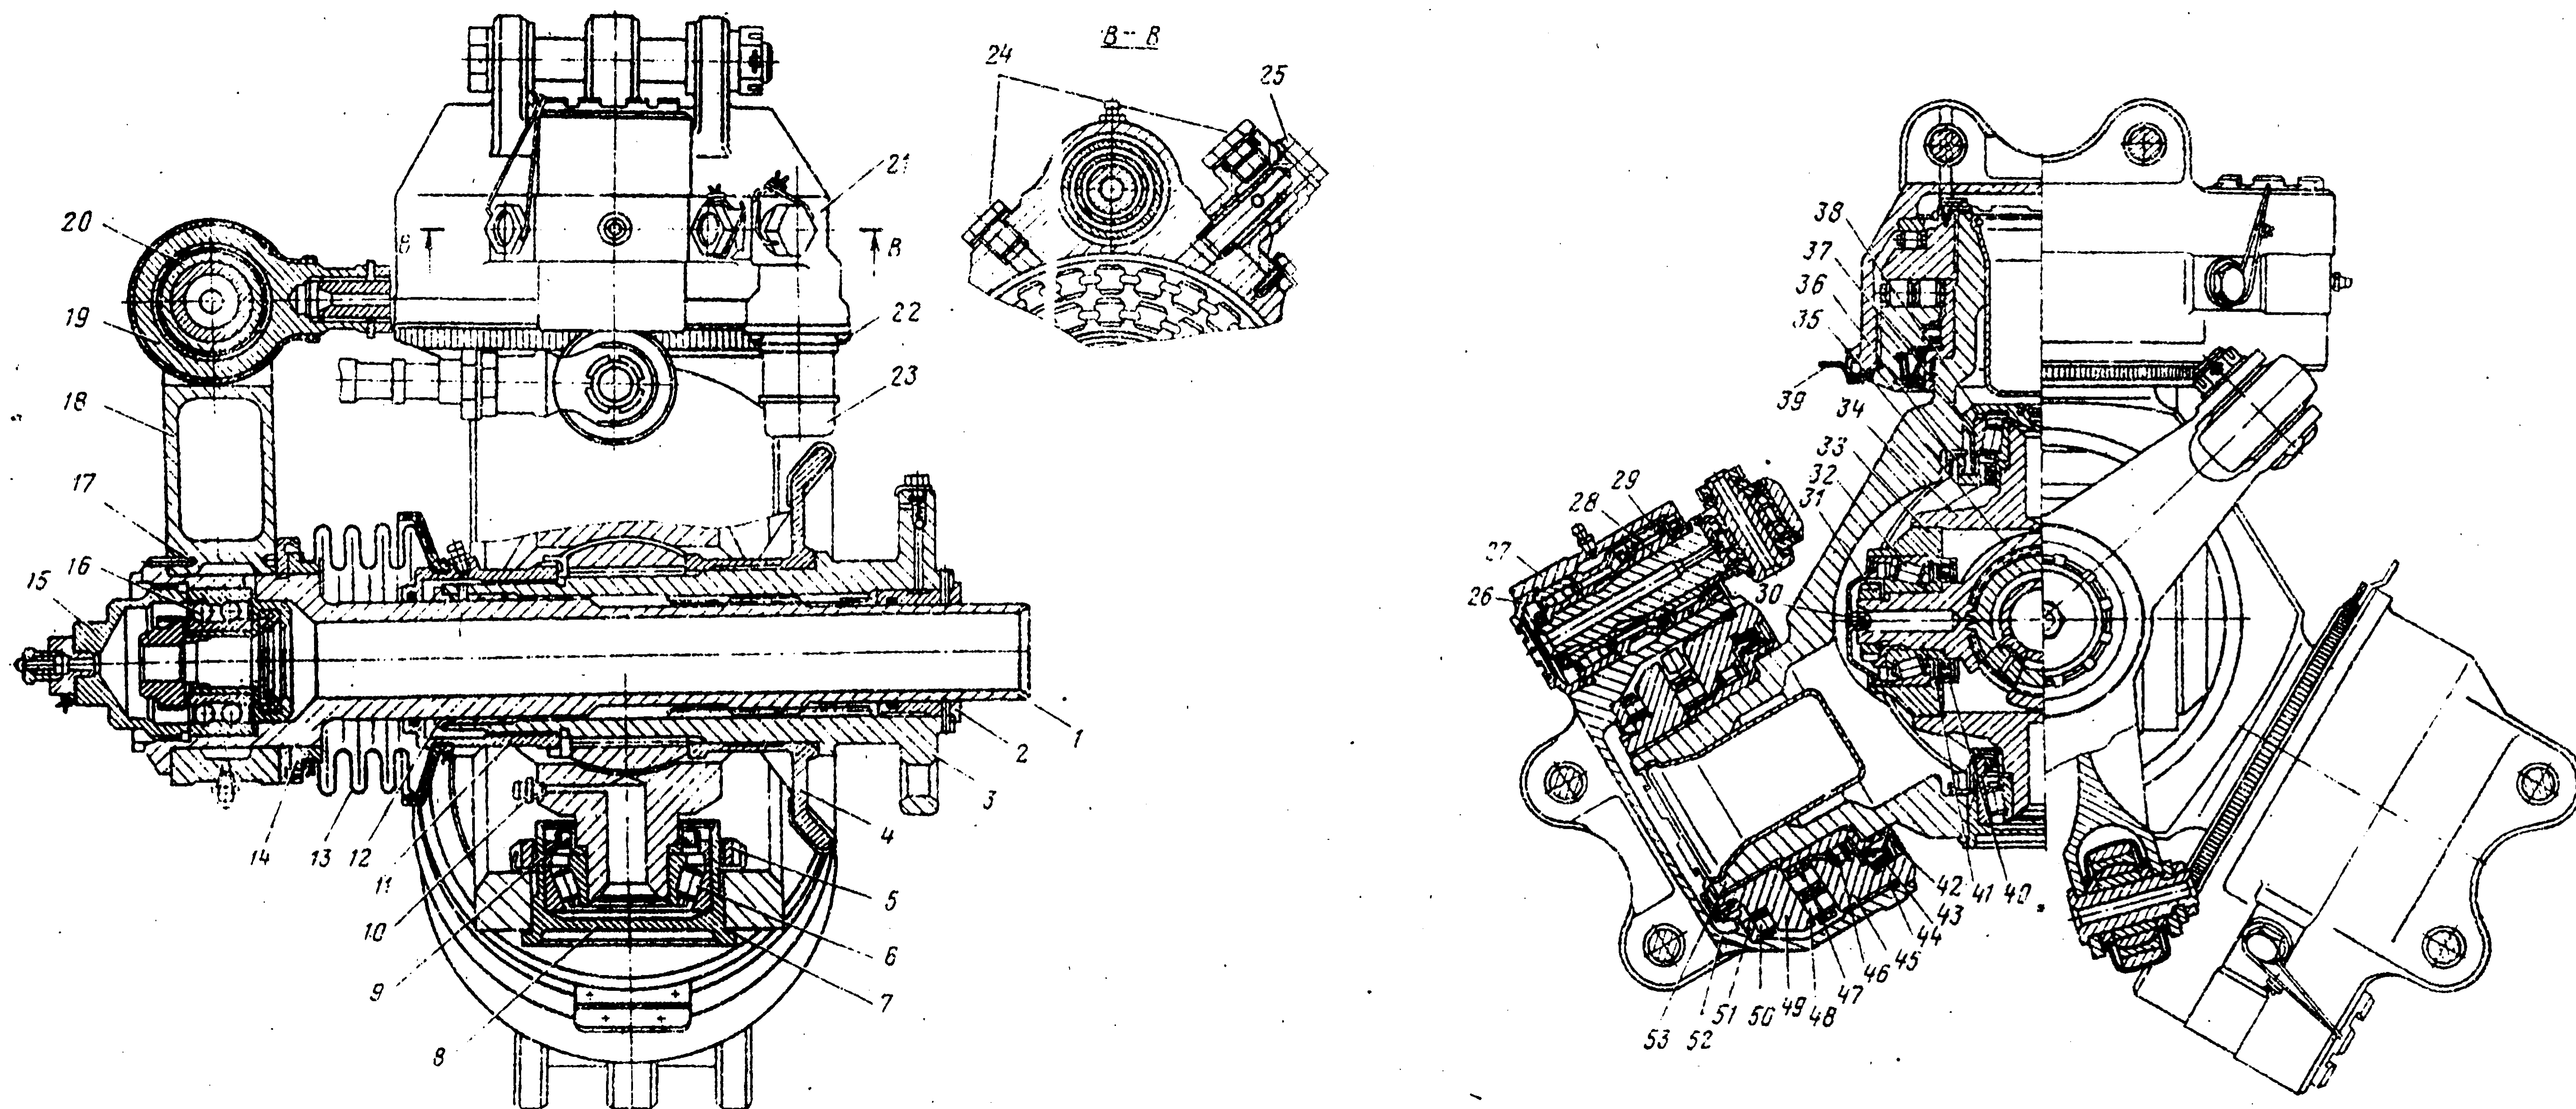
Втулка хвостового винта: 1 — ползун; 2, 12, 53 — втулки; 3 — ступица; 4 — ограничитель взмаха; 5, 11, 14, 31, 36, 45, 49 — гайки; 6, 32, 46, 48, 50 — роликовые подшипники; 7, 38, 41 — регулировочные кольца; 8, 33, 37 — стаканы роликоподшипников; 9, 40, 43 — армированные манжеты; 10 — пресс-масленка; 13 — резиновый чехол; 15 — резьбовая крышка; 16, 27 — шариковые подшипники; 17 — штифт; 18 — поводок; 19 — регулировочная тяга; 20 — сферический шарнирный подшипник; 21 — масляный бачок; 22 — болт; 23 — колпачок; 24 — пробки; 25 — специальный винт; 26 — колпачковая гайка; 28 — валик; 29 — игольчатый подшипник; 30 — крышка; 34 — корпус кардана; 35 — траверса; 39 — шайба; 42, 44 — уплотнительные кольца; 47 — упорное кольцо; 51 — кольцо упорного подшипника; 52 — корпус осевого шарнира
